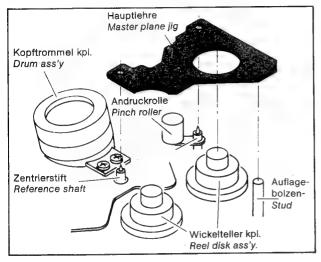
Hauptlehre Fig. 2-15 Master plane jig
